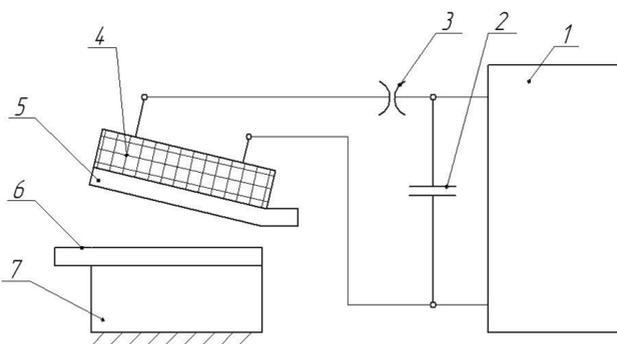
Схема магнитно-импульсной сварки:
